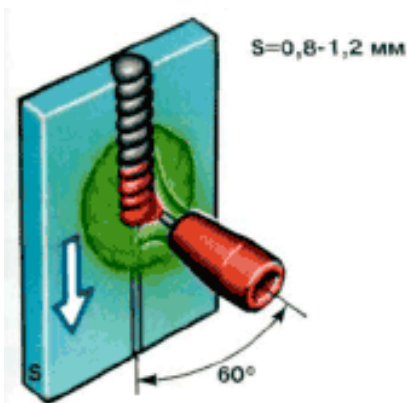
Схема установки полуавтомата для сварки в среде углекислого газа:
